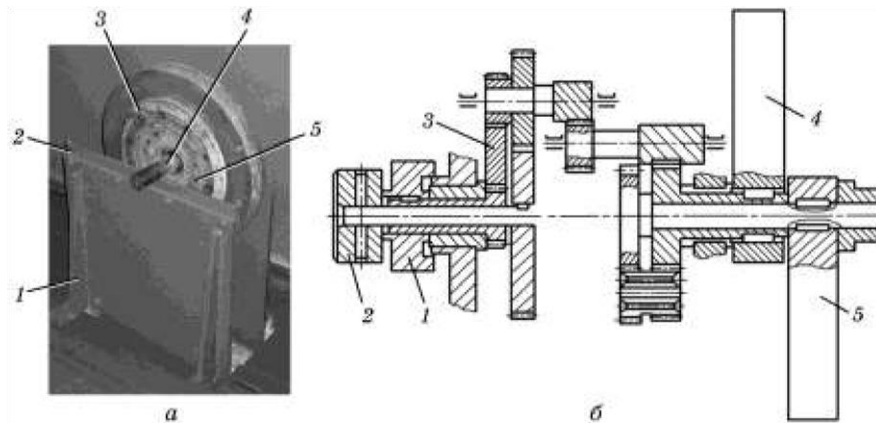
Зовнішній вигляд пристрою для статичного балансування (а) і схема пристрою для автоматичного балансування шліфувального круга на верстаті (б).
